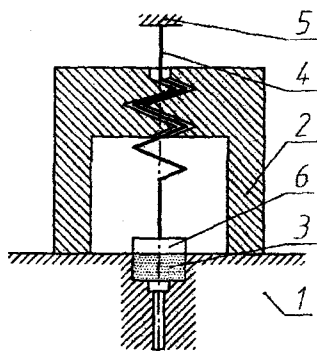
Штамп для нагружения заготовки осевым сжатием и сдвигом
